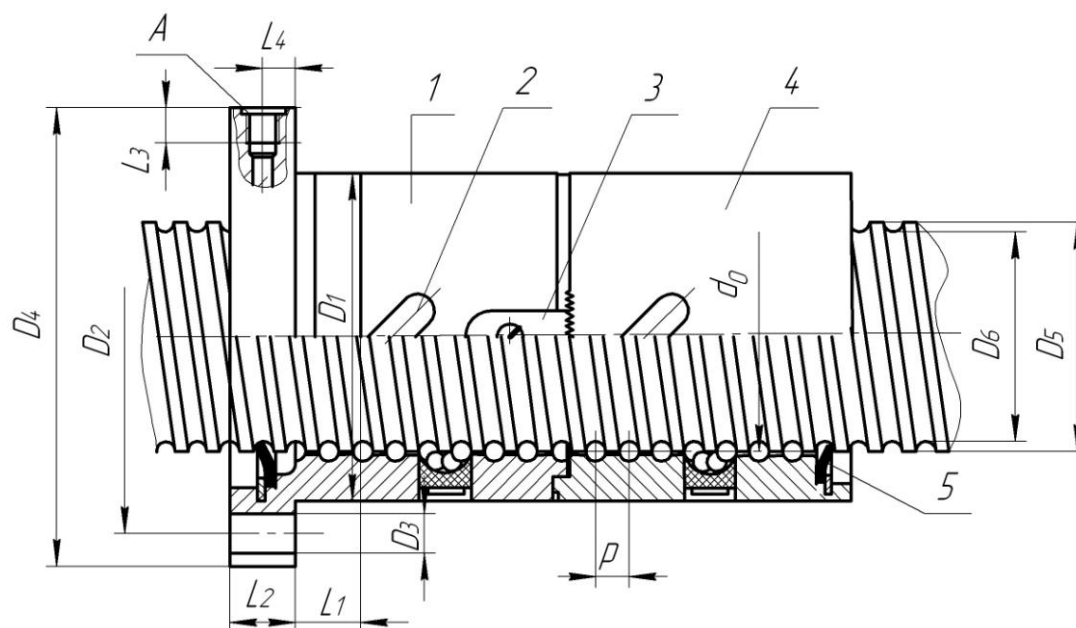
Передача з двома гайками за DIN 69051
